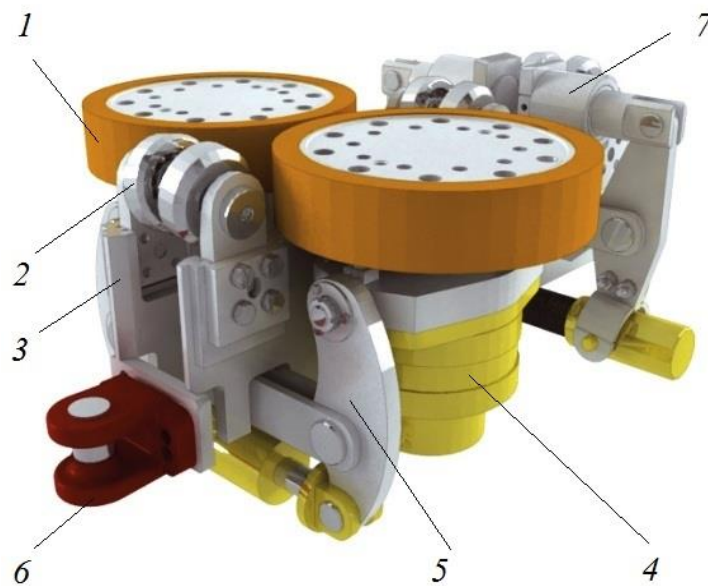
Общий вид тягового устройства подвешенного монорельсового локомотива BECKER KPCS-148 [297]: 1 – приводное колесо; 2 – ходовое колесо; 3 – рама тележки; 4 – привод; 5 – прижимной механизм; 6 – сцепка; 7 – тормоз
